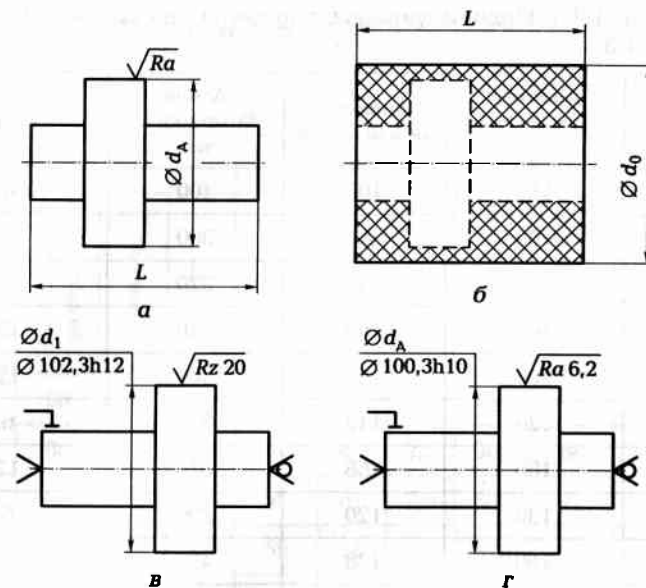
Схема обработки наибольшей по диаметру ступени вала: а — вал; б — заготовка; в — обтачивание; г — шлифование
